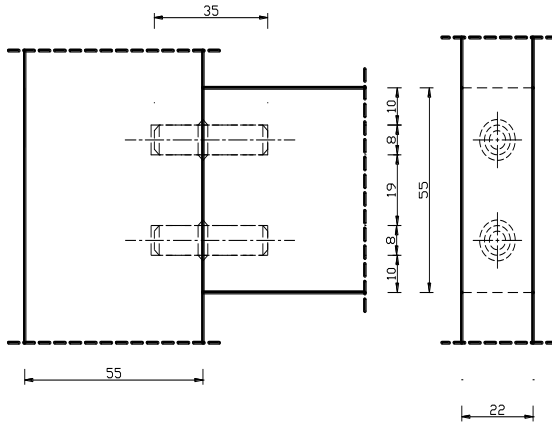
Deney örneklerinde kullanılan maksifiks bağlantı elemanı
